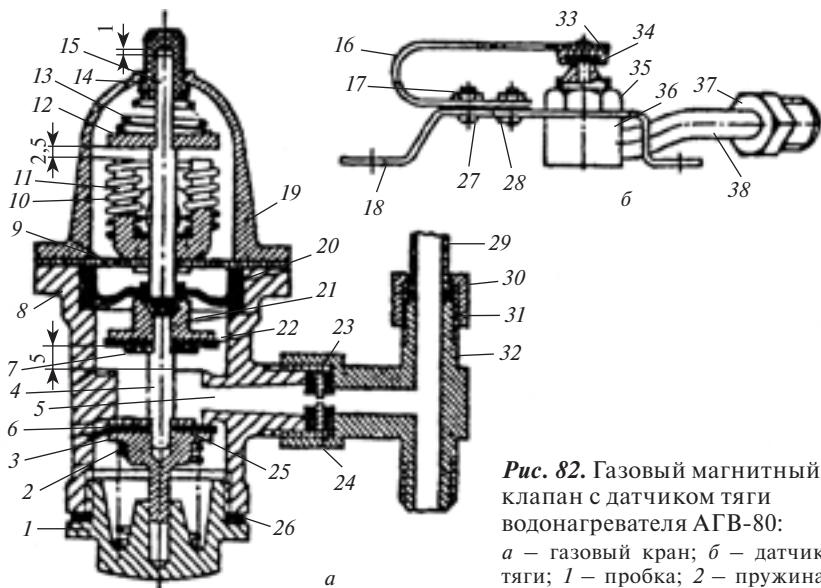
Газовый магнитный клапан с датчиком тяги водонагревателя АГВ-80:
